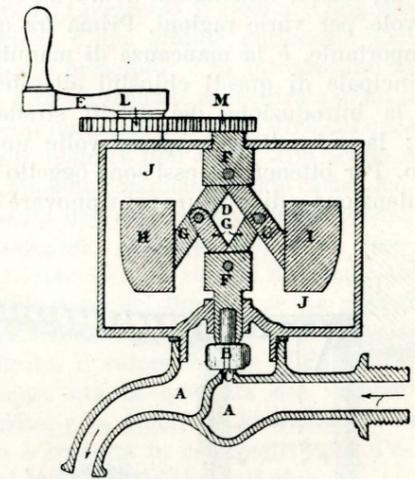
Sezione del rubinetto intermittente sistema Bayard.
